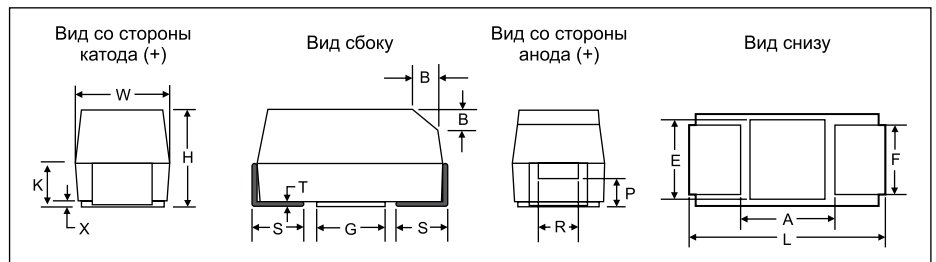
Габаритный чертеж танталового конденсатора для поверхностного монтажа
